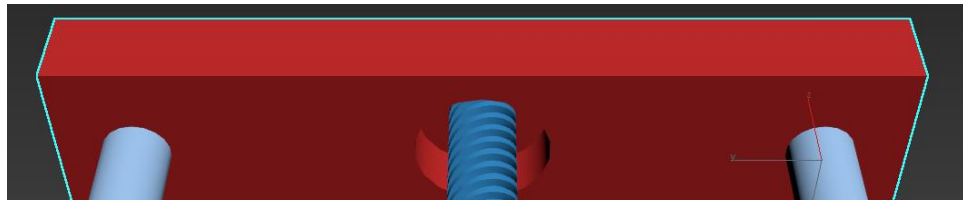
Моделювання посадкового місця для підшипника
